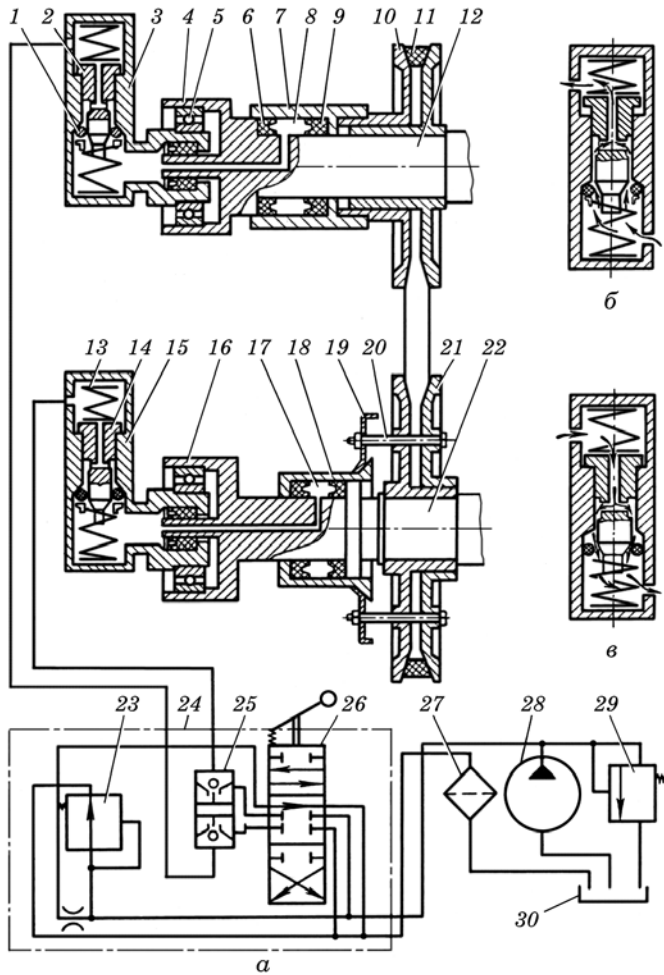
Принципова схема гідроприводу рухомого диска шківів варіатора молотильного барабана комбайна «Нива»:
